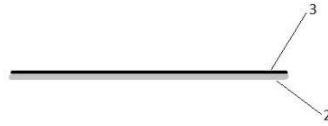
Центральная пластинка. Вид сбоку. 2, внутренний слой пластинки из дюспо; 3, наружный слой пластинки из флиса.
